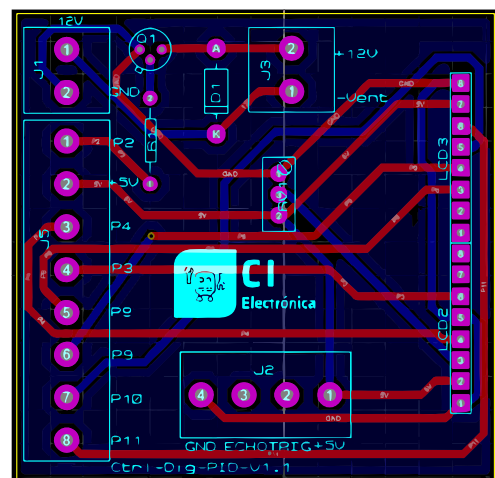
Diseño de la disposición de componentes de la placa PCB.
